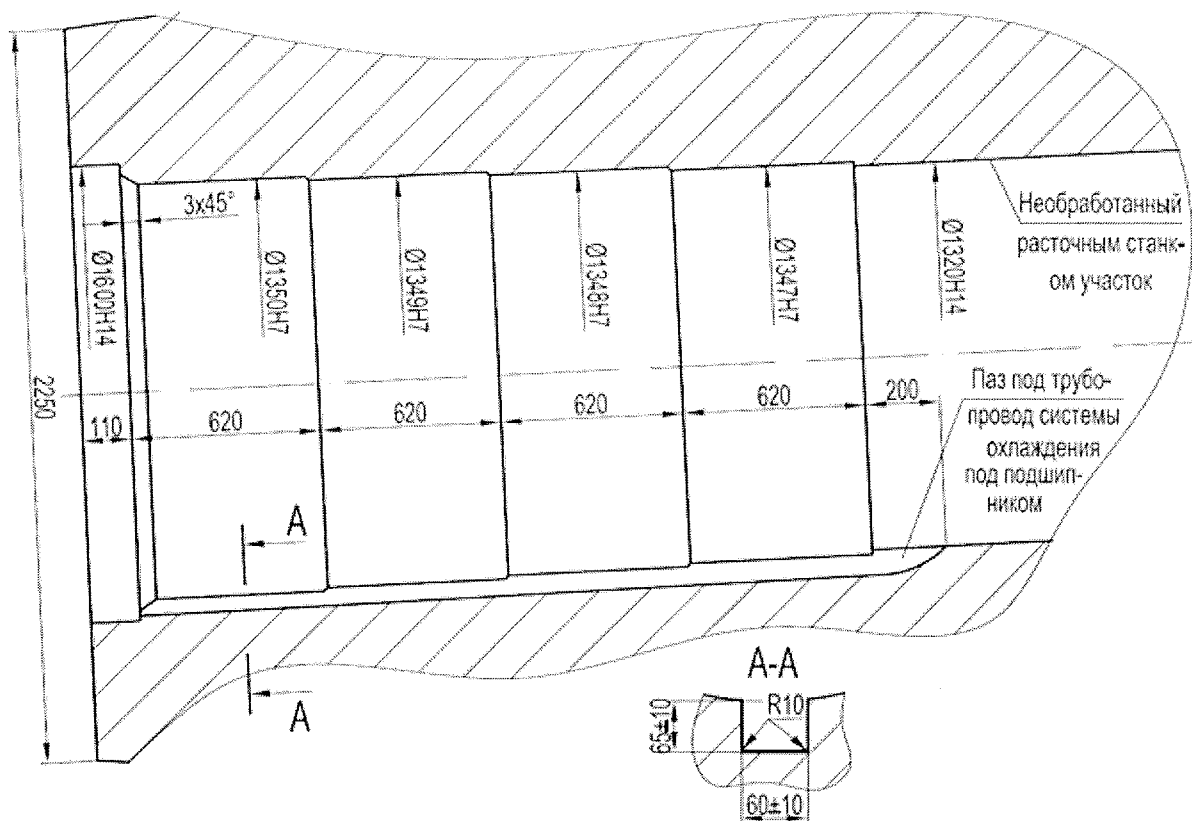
Ориентировочные размеры расточки кронштейна под запрессовку кормового дейдвудного подшипника
